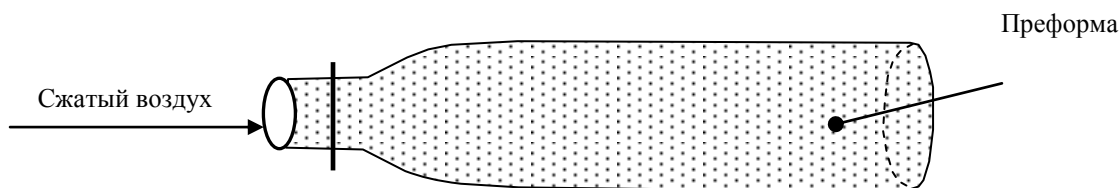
Заготовка для раздува полимерных бутылок (преформы)
